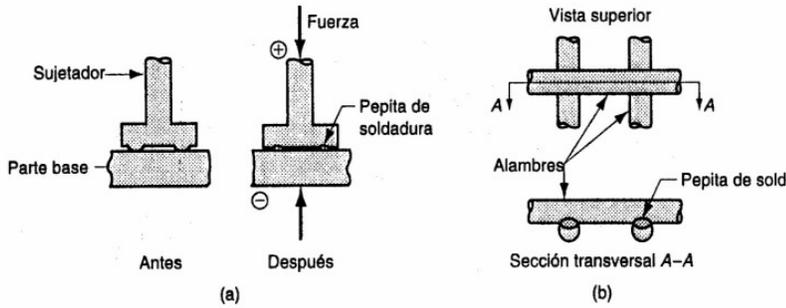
Dos variables de soldadura por proyección: (a) soldadura de un sujetador maquinado o formado sobre una parte de chapa de metal y (b) soldadura de alambre transversal.
